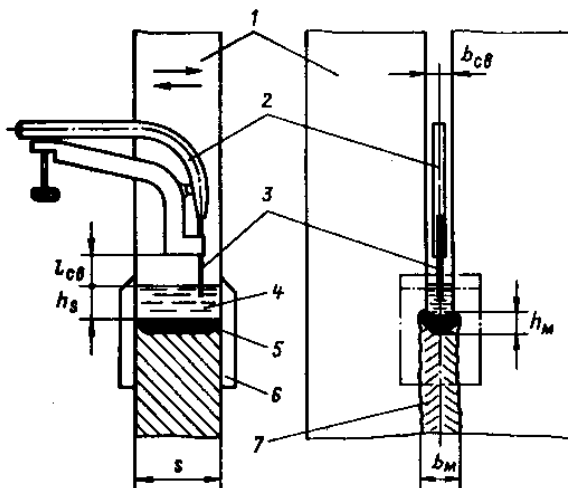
Схема электрошлаковой сварки:
